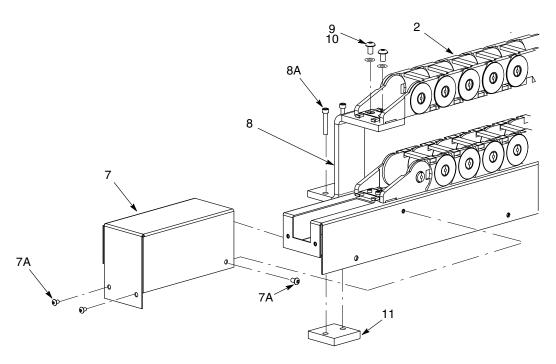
Instalación del soporte Z y la cubierta de la cadena de cable
